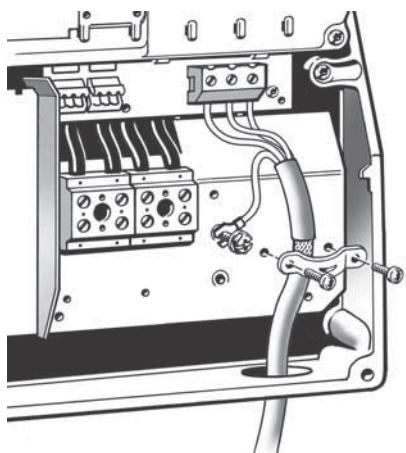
Motoranschluss, Gehäuse B1 und B2
